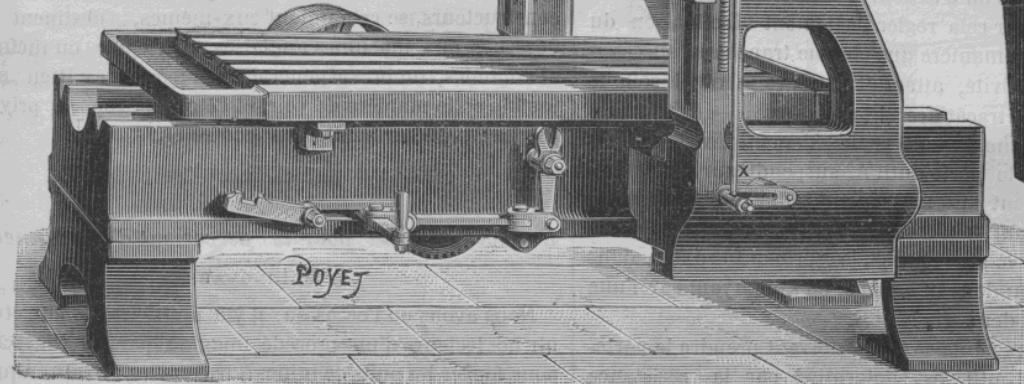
Machine à raboter muni du porte-outil reversible.
